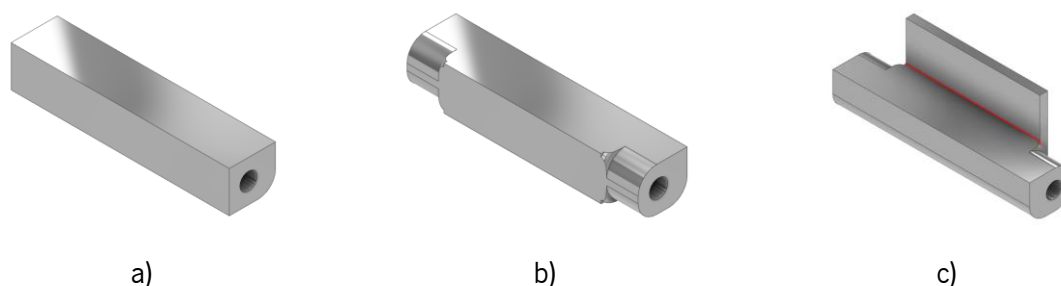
Perfil da dobradiça do alçapão extrudido, maquinado e soldado respetivamente em a), b) e c).
